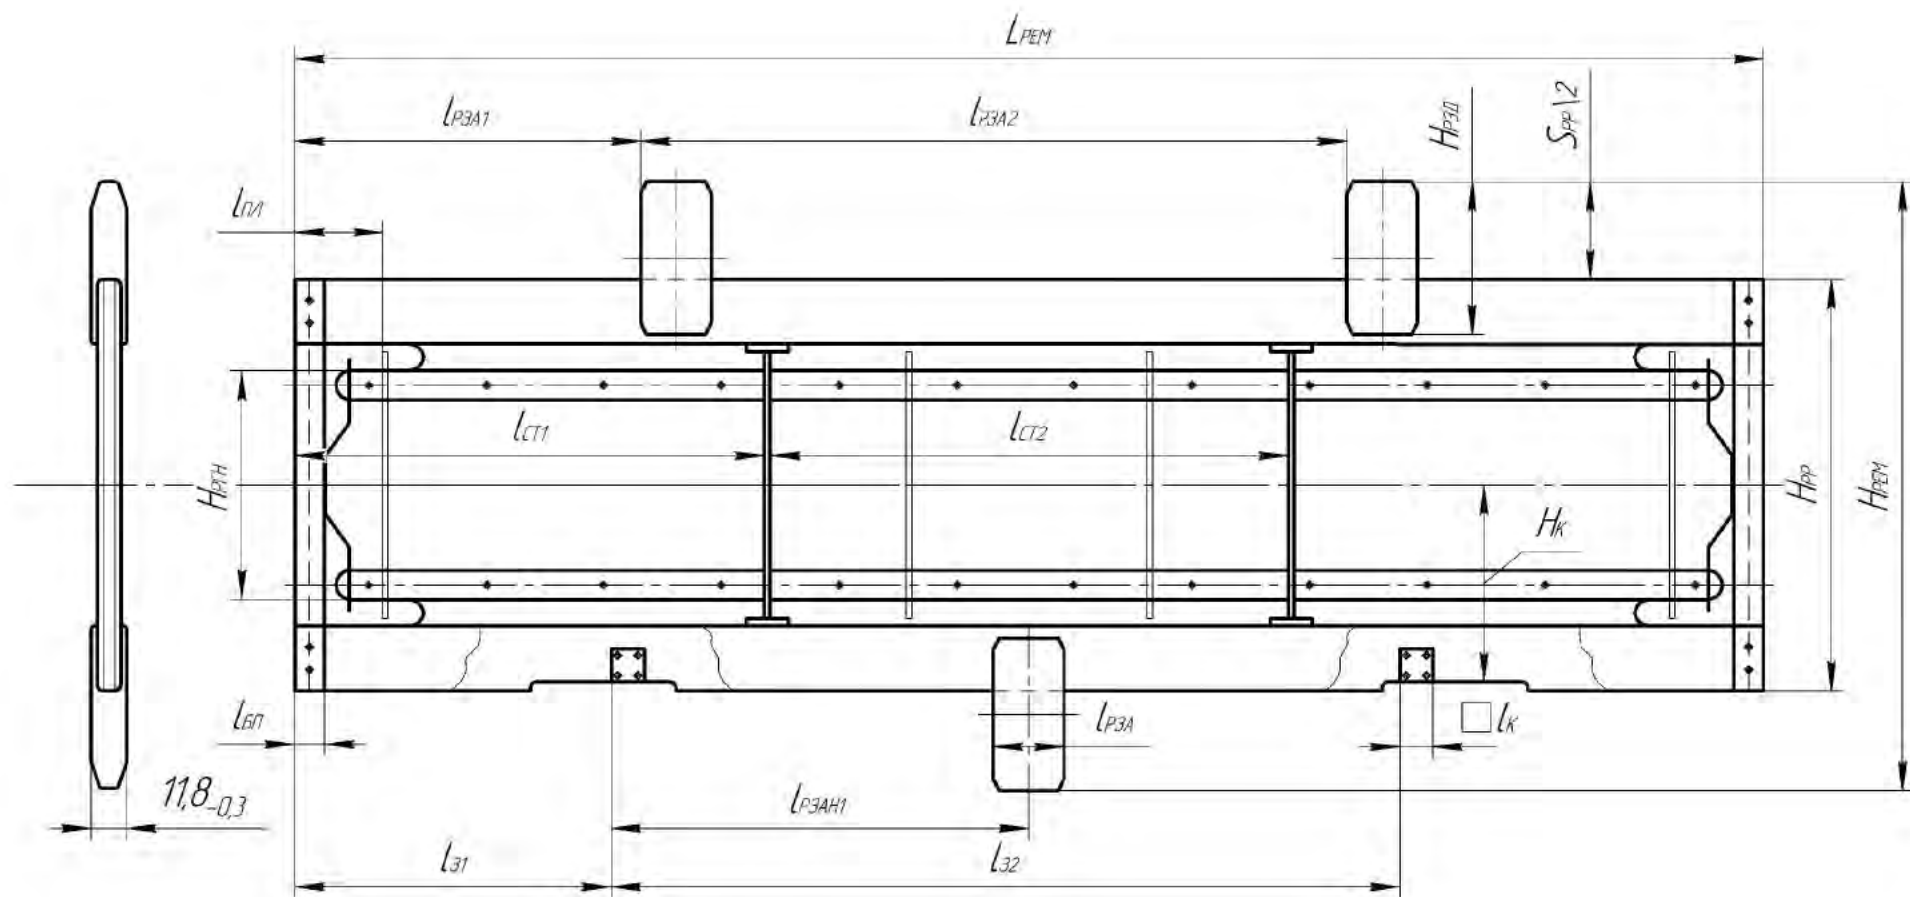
Конструкция узла крепления ремизной рамы с захватами (крючками) ползунов механизма её привода МРД
